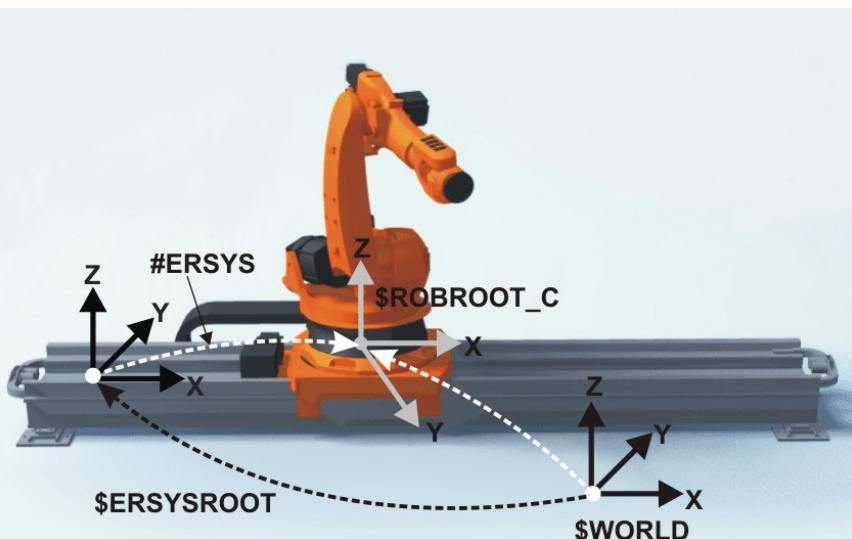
Unidad lineal de la cinemática ROBROOT
